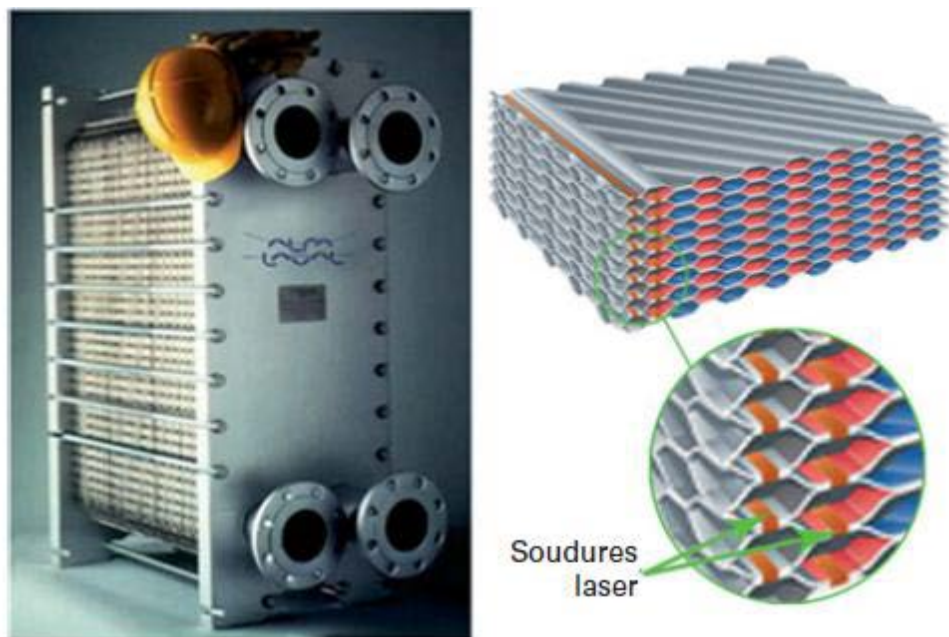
Échangeur à plaques tout soudé.
